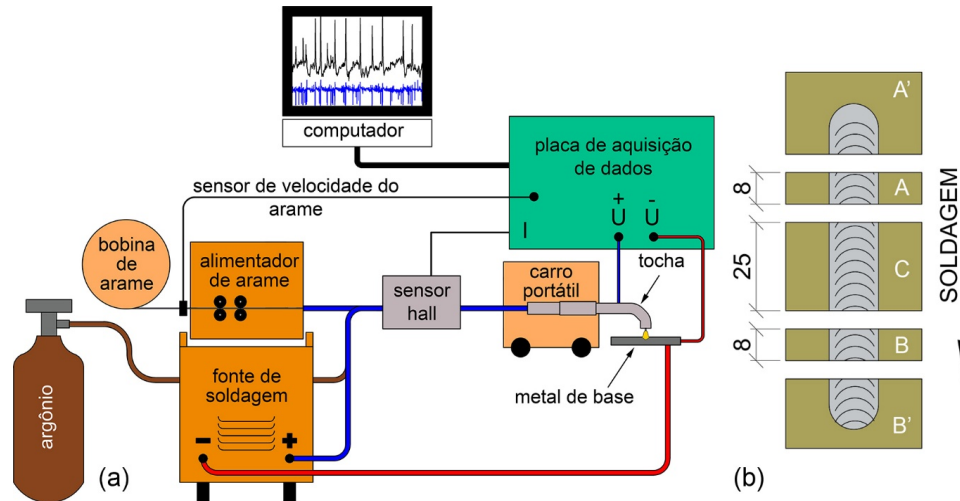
(a) Representação esquemática da soldagem dos arames tubulares; (b) Esquema de corte das amostras.
